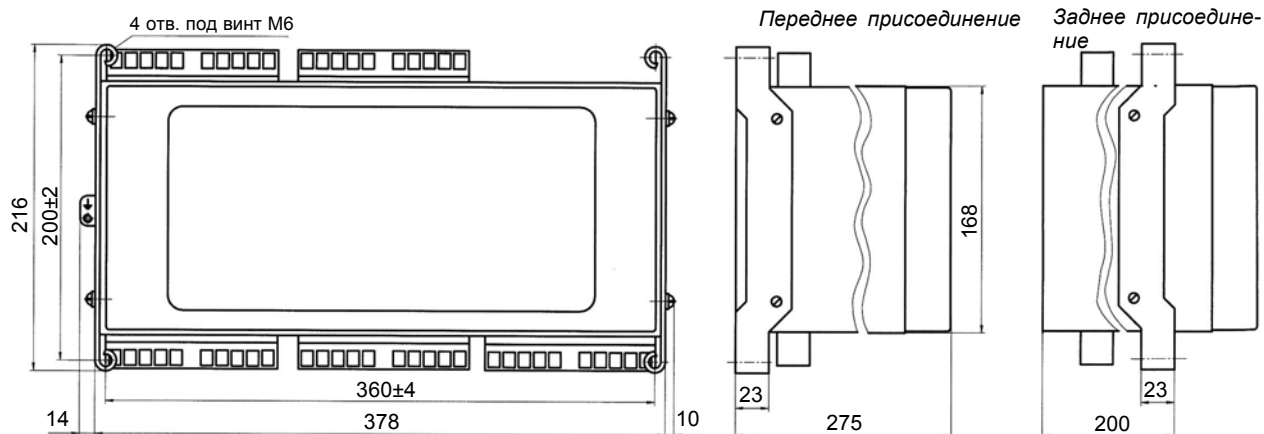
Габаритные, установочные размеры блока типа БЭ 2603
